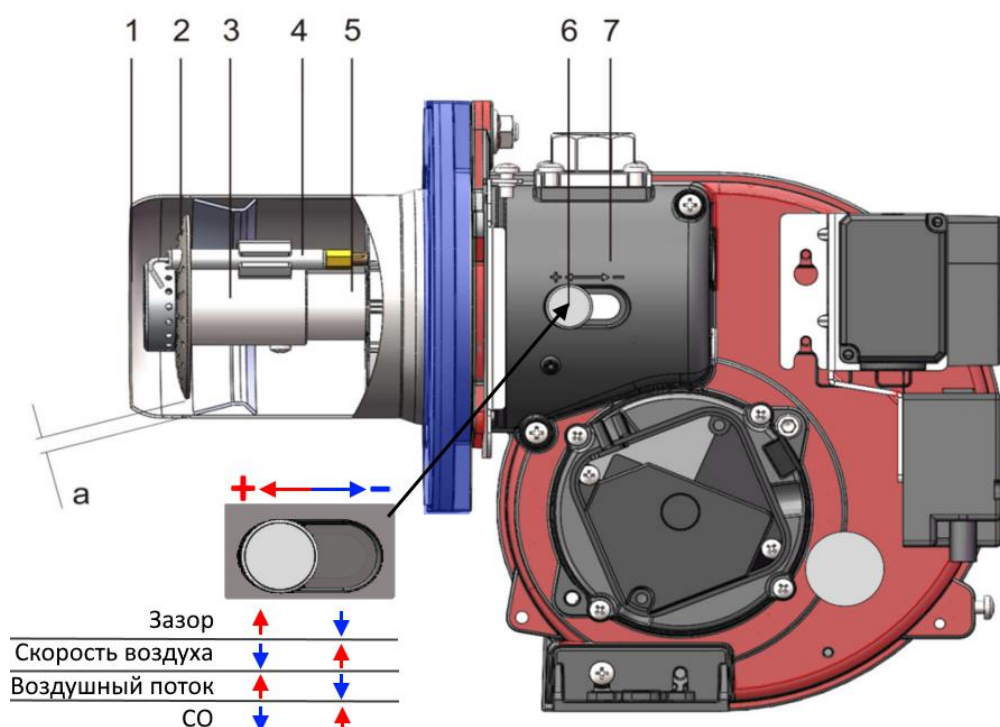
Регулировка сопловой сборки горелки ЕММА-СО.2-Г. 1 – Оголовок горелки; 2 – Диффузор воздуха; 3 – Газовое сопло; 4 – Электрод розжига; 5 – Газовая труба; 6 – Болт регулировки положения диффузора воздуха; 7 – Индикатор регулировки; а - Зазор между диффузором воздуха и конусом трубы горелки.
